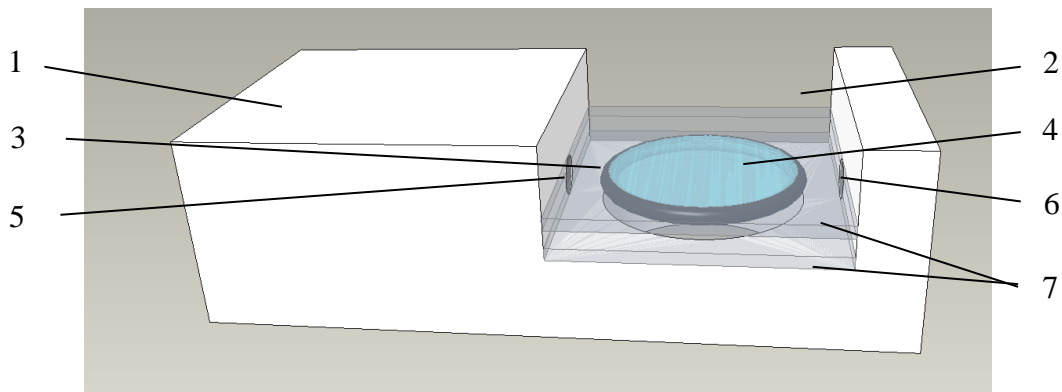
Model testovacího přípravku, pohled shora: 1 – tělo testovacího přípravku, 2 – výřez pro umístění podložního sklička, 3 – teflonový kroužek, 4 – roztok polymeru
